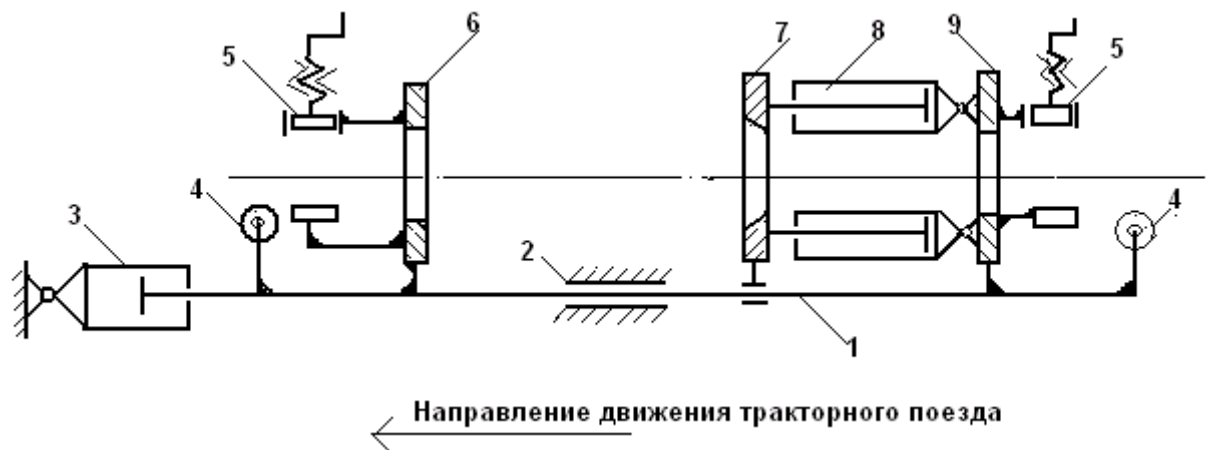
Гидравлическая установка для соединения труб методом прессовой посадки; 1 – подвижная рама; 2 – направляющие; 3 – гидроцилиндр перемещения рамы; 4 – роликовая опора; 5 – зажим фильерной плиты; 6 – передняя плита; 7 – подвижная плита; 8 – рабочие гидроцилиндры; 9 – задняя плита.
